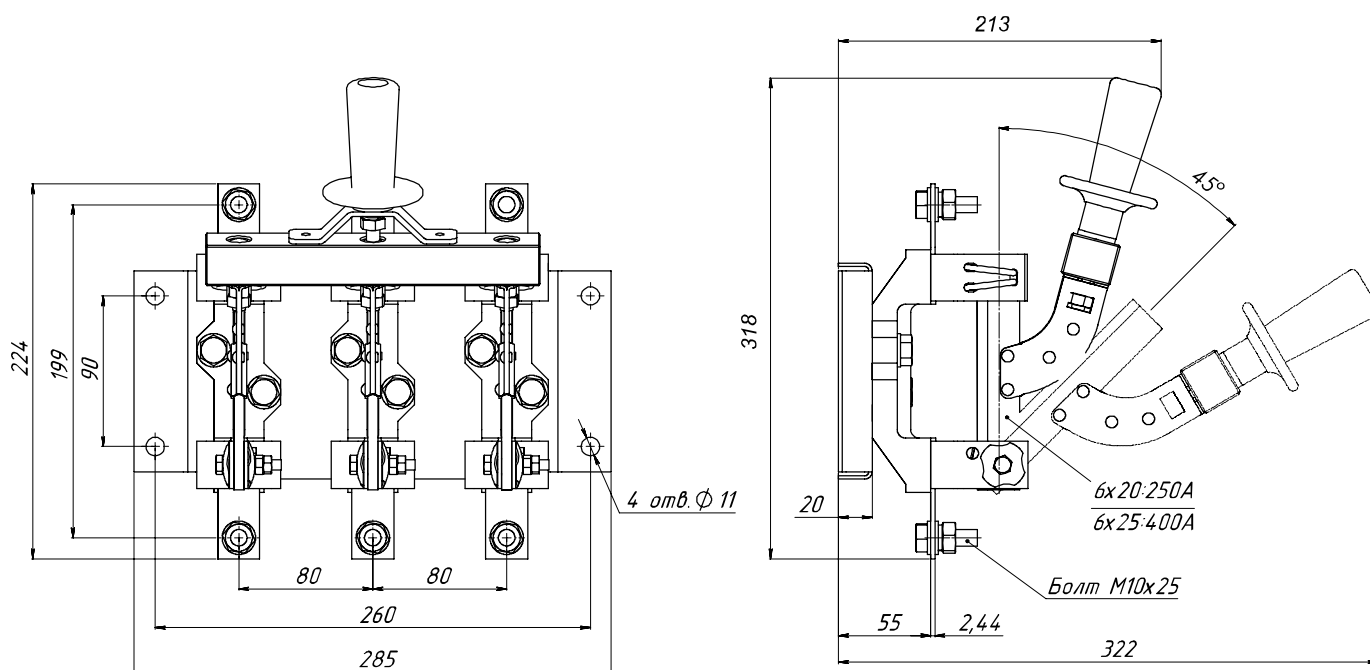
Разъединитель PE19 трехполюсный с центральной рукояткой, переднего присоединения шин
